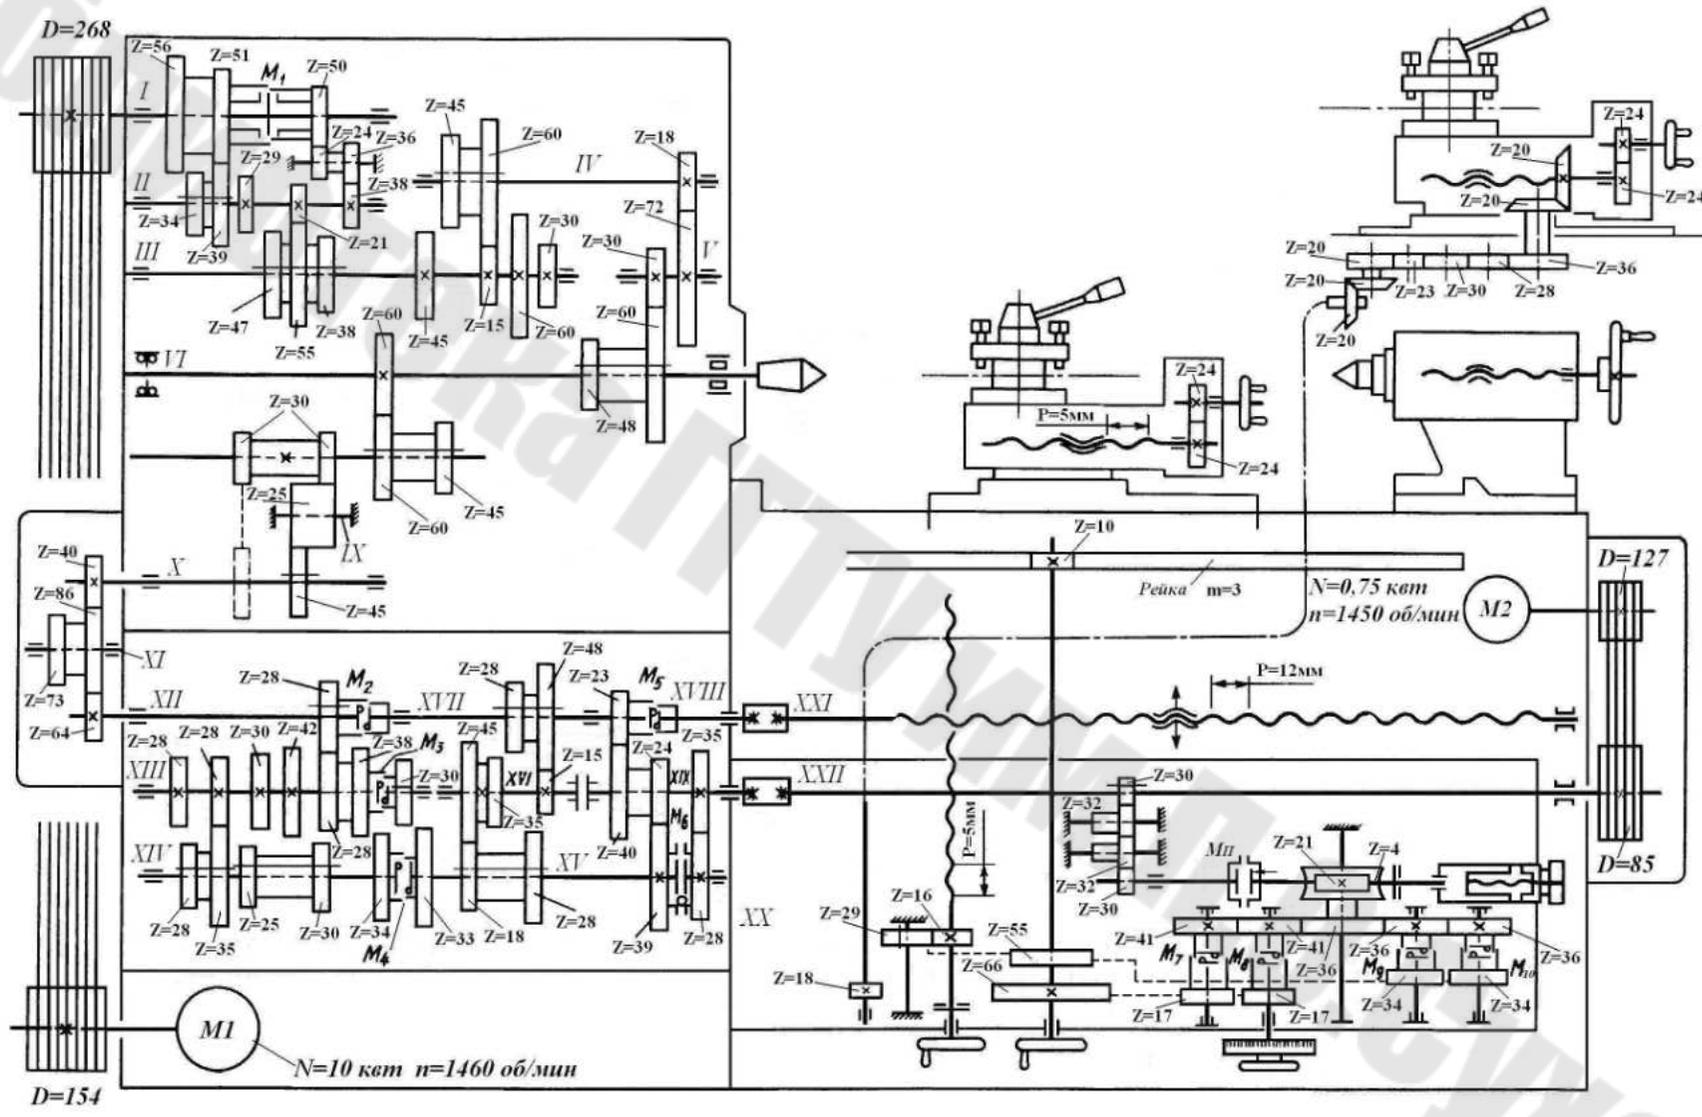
Кинематическая схема токарно-винторезного станка 16K20
